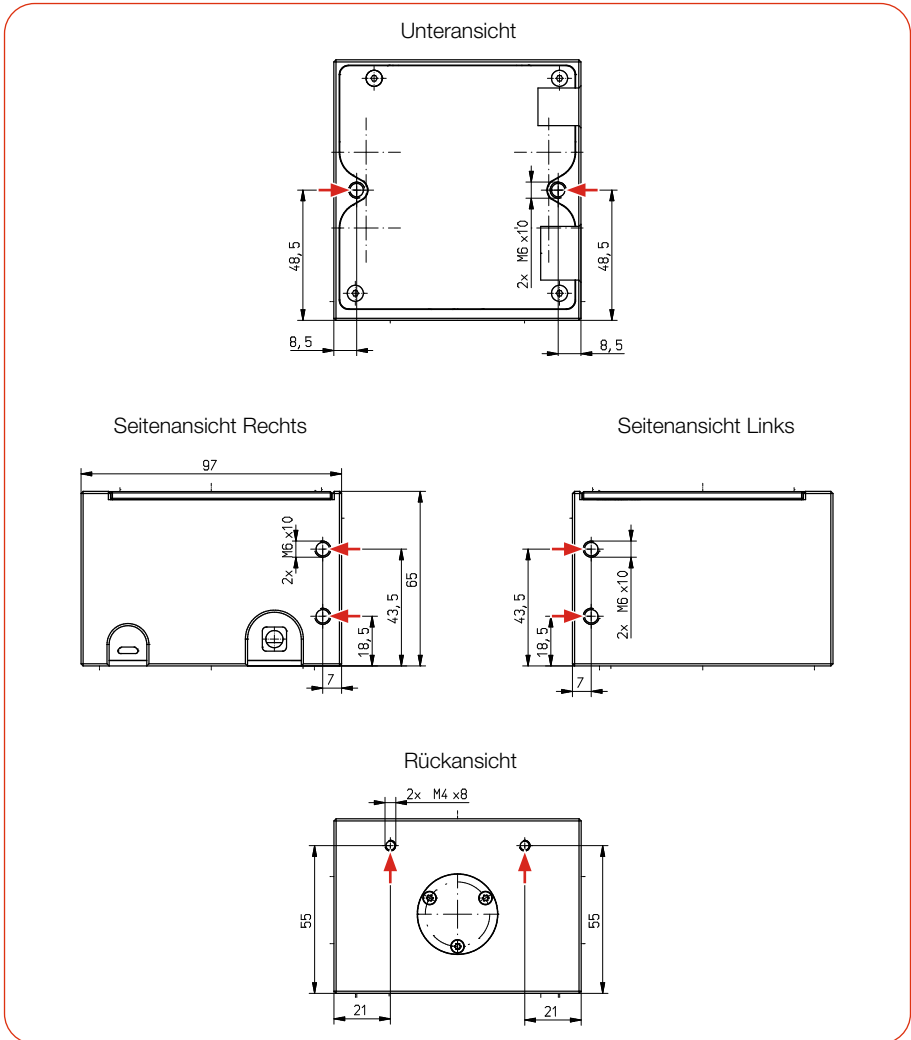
Befestigungsgewinde im Gehäuse (Maße in mm)
